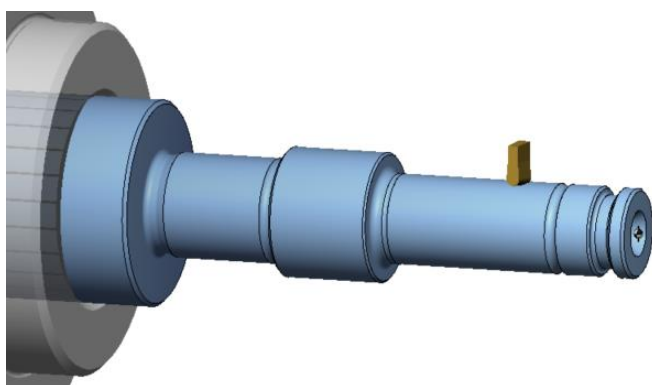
Hrubování průměru zapichovacím nožem.
